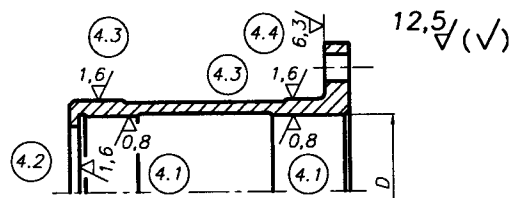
Рекомендуемая шероховатость поверхностей
